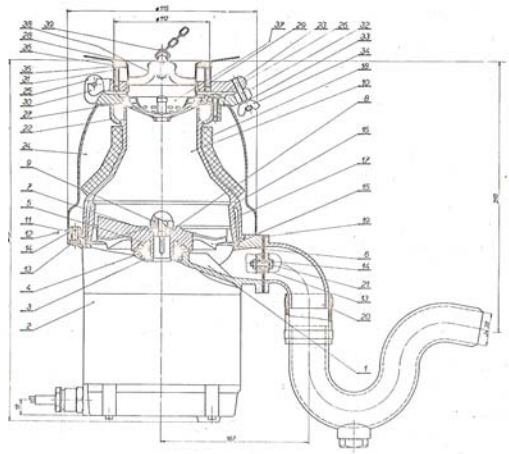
Princíp mokrého systému zhromažďovania odpadu Matthew-Hall
